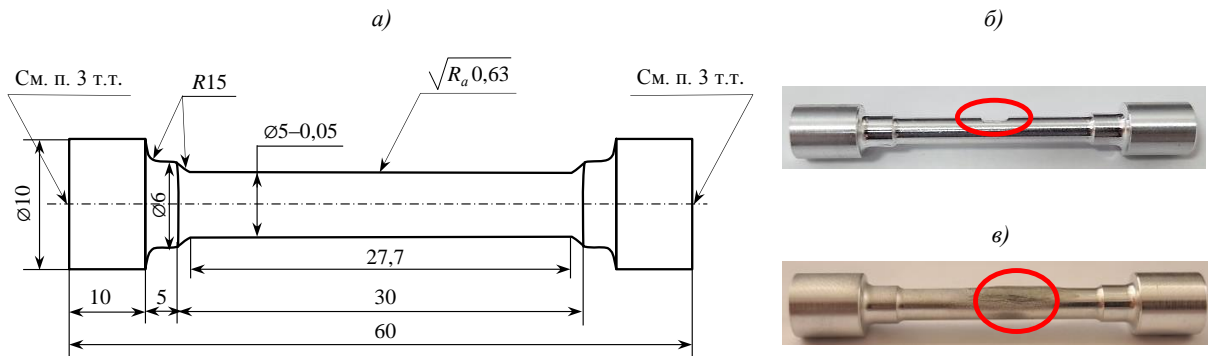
Эскиз (а) и изготовленные образцы для проведения механических испытаний до (б) и после (е) напыления порошковой композиции
